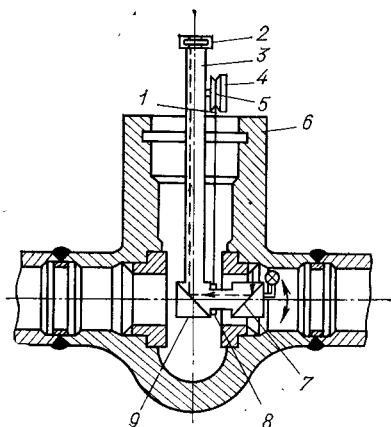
Прибор для осмотра колец корпуса задвижки:
